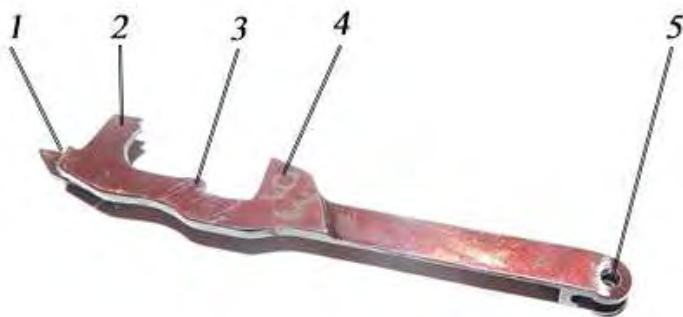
Спусковая тяга: 1 – зуб самовзвода; 2 – зубья;
